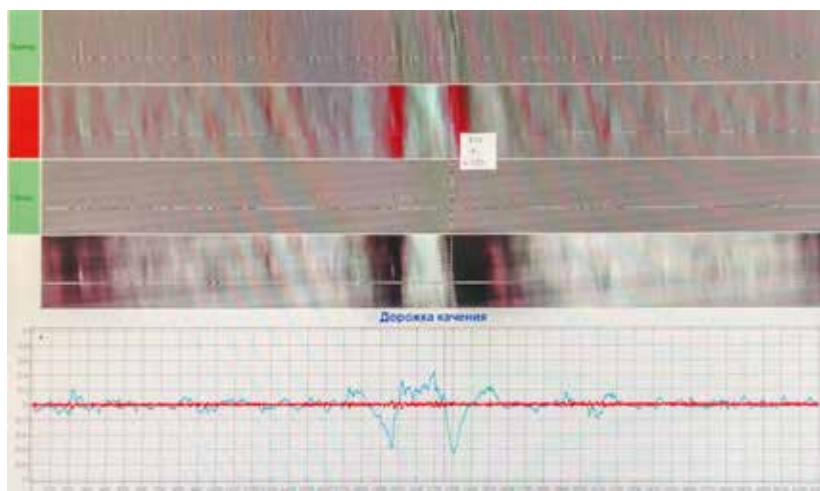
Сканограмма поверхностного дефекта «локальный шлифовальный прижог» на дорожке качения наружного кольца буксового вагонного подшипника 42726
